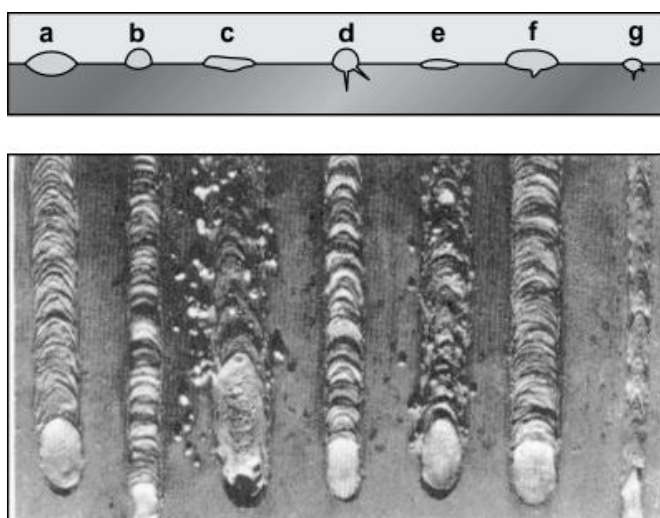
Efeito dos parâmetros de soldagem no aspecto do cordão de solda
